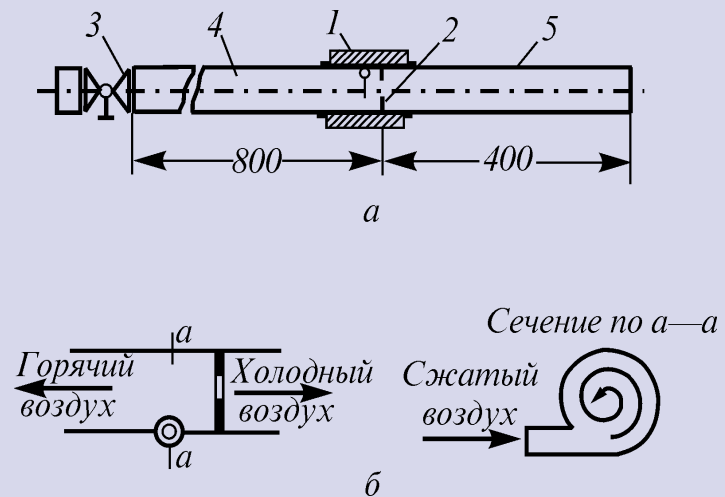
Вихревая труба: а — конструкции; б — схема протекания воздуха; 1 — сопло; 2 — диафрагма; 3 — дроссельный вентиль; 4 — горячий конец трубы; 5 — холодный
